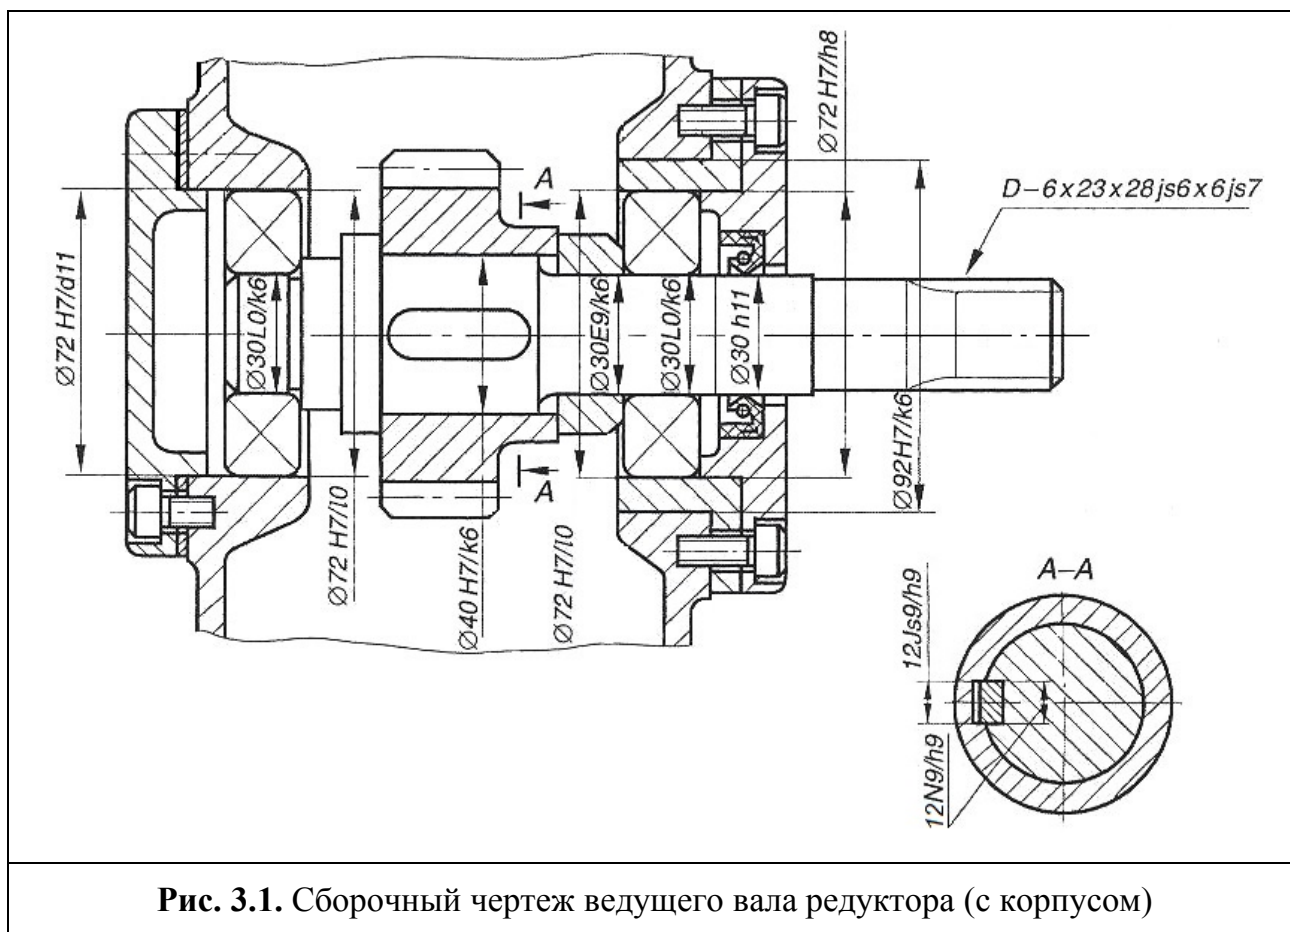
Сборочный чертеж ведущего вала редуктора (с корпусом)
